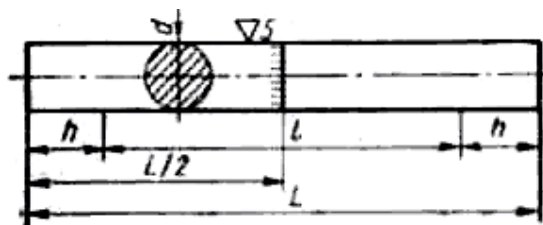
Форма образцов для испытания стыковых соединений стержней
